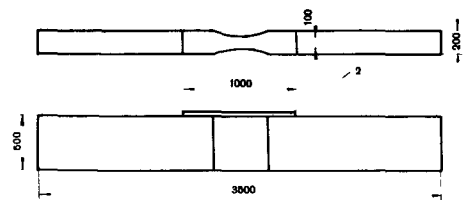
Крупногабаритный образец: 1 — основной металл; 2 — наплавка
